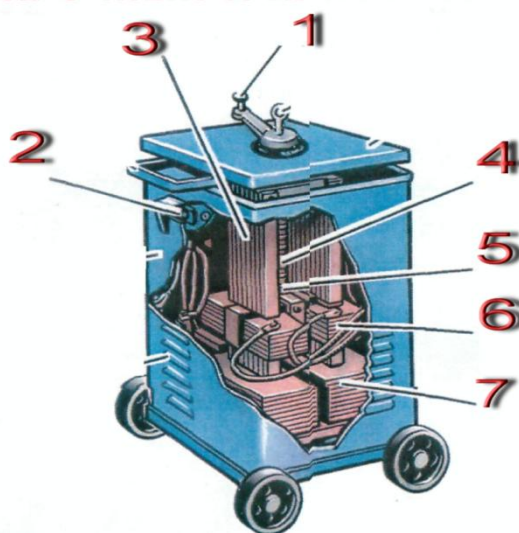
Сварочный трансформатор ТСК-500
